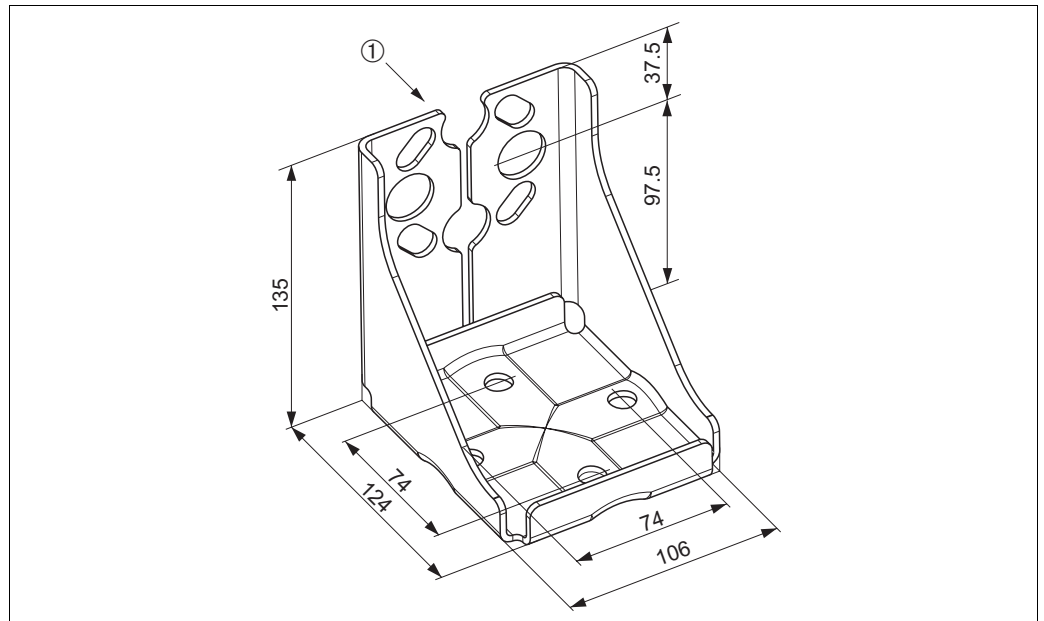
Montagehalterung für Wand- und Rohrmontage
